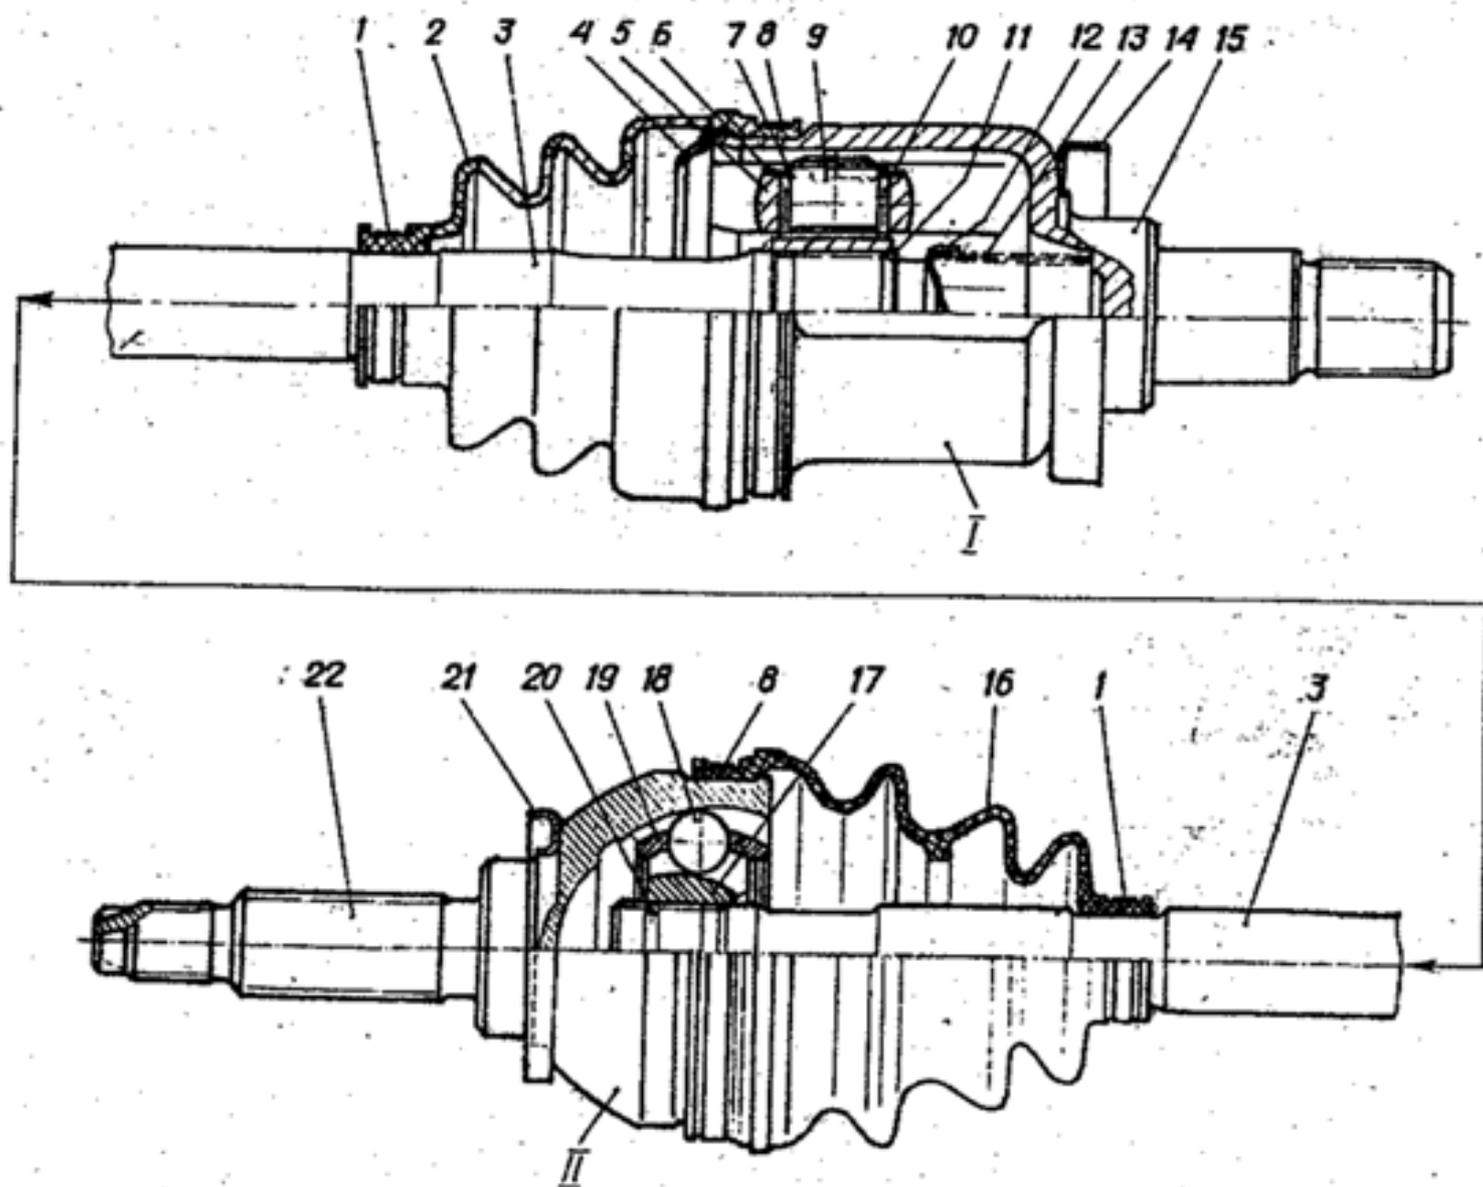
Шарнирный вал: 1 - хомут малый; 2 - чехол; 3 - вал шарниров; 4 - чашка внутреннего шарнира; 5 - ролики; 6 - шайба упорная; 7 - кольцо стопорное; 8 - хомут большой; 9 - трехшиповик; 10 - иголка подшипника; 11 - кольцо стопорное; 12 - чашка пружины; 13 - пружина поджимная; 14 - грязеотражатель; 15 - корпус внутреннего шарнира; 16 - чехол; 17 - обойма внутренняя; 18 - шарик; 19 - сепаратор; 20 - кольцо стопорное; 21 - грязеотражатель; 22 - корпус наружного шарнира.
